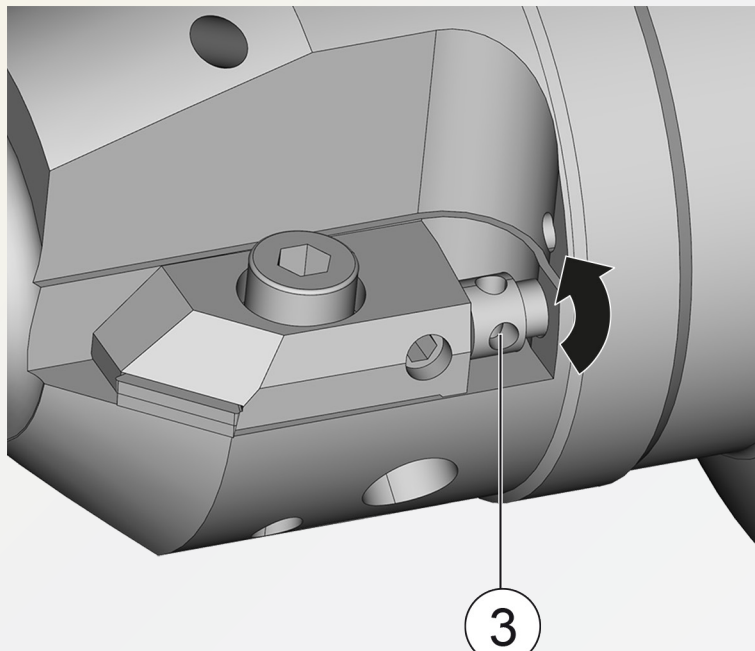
WSP mit der Längeneinstellschraube axial auf das Sollmaß einstellen
